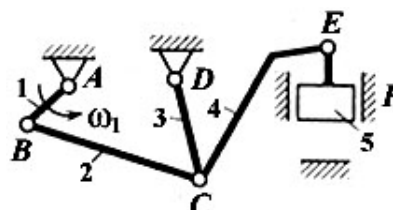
Механизм ковочно-штамповочного прессы
